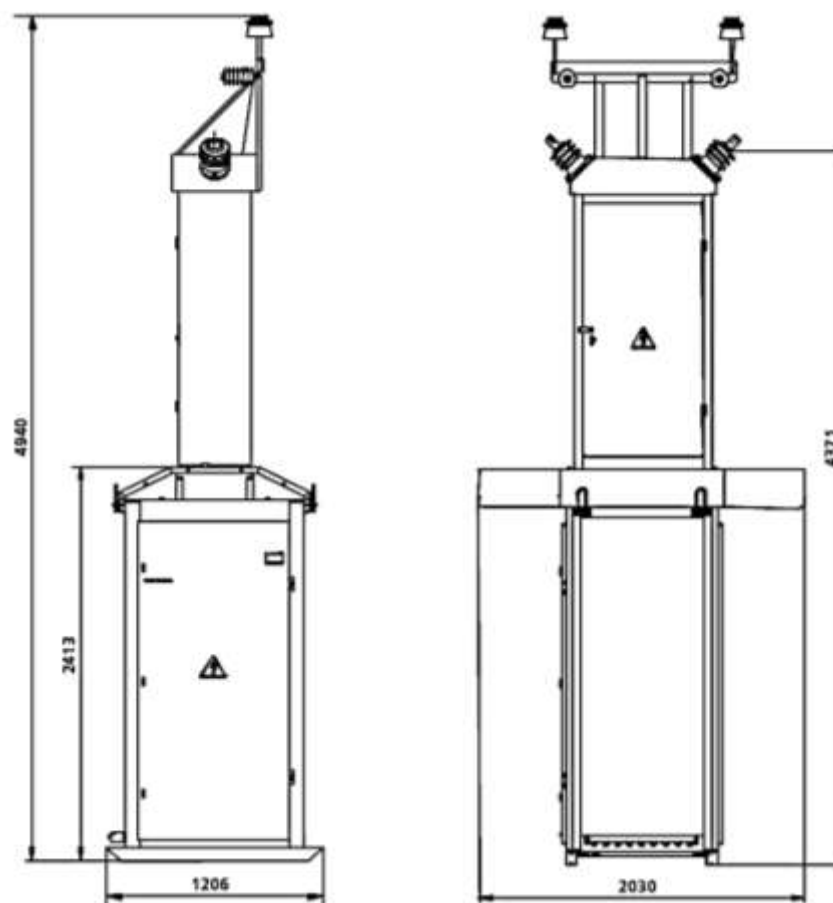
Общий вид и габаритные размеры УКЗВ
